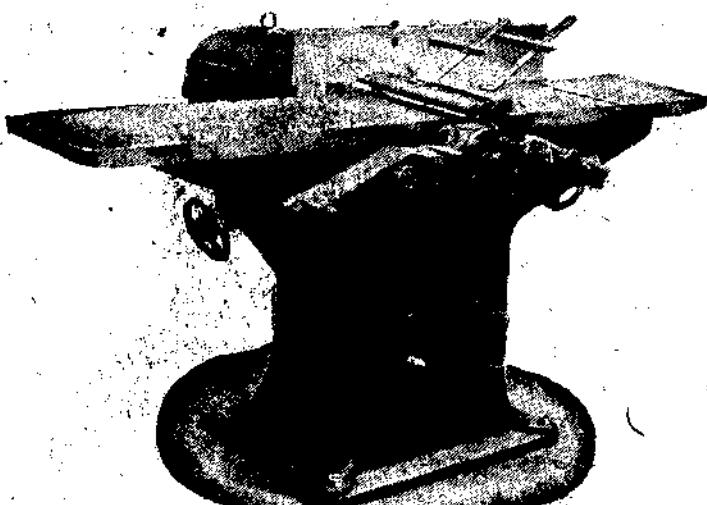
Универсальный пригонный, строгальный, фуговочный и калевочный станок.
